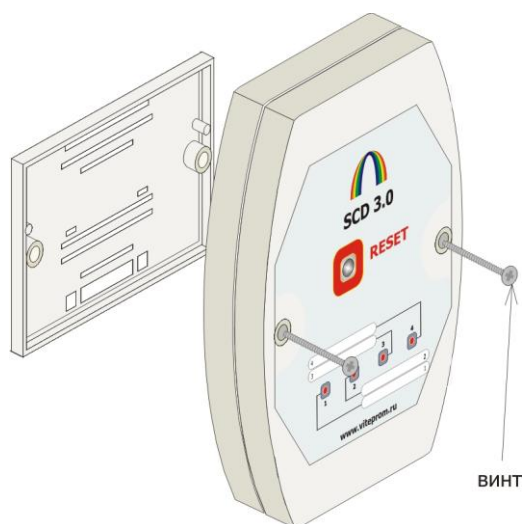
Монтаж блока SCD 3.0 на DIN-рейку
